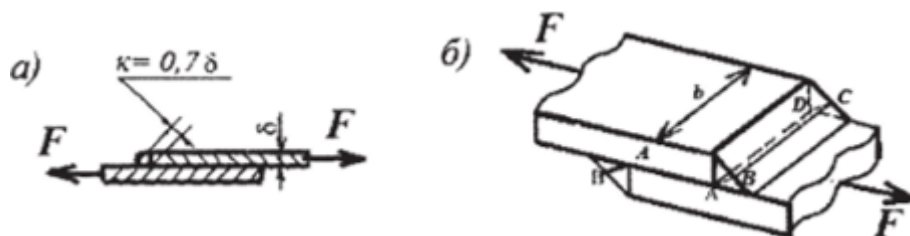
Схема сварного соединения: а) расчетная схема углового шва; б) площадь среза $ABCD$ сварного шва
